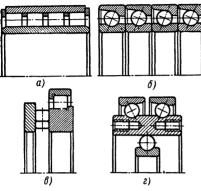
Комбинированные подшипники качения: а — роликоподшипник радиальный с короткими цилиндрическими роликами, четырехрядный; б — подшипниковый блок из четырех радиально-упорных шарикоподшипников; в — радиально-упорный роликоподшипник; в — двойной шарикоподшиник принудичельным вращением среднего кольца
